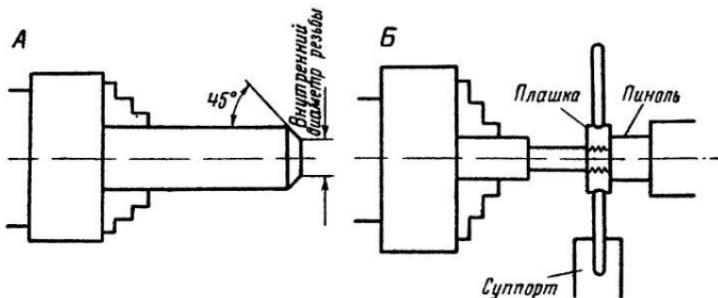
Нарезание резьбы плашкой на токарном станке: А — подготовка заготовки; Б — предупреждение перекоса плашки.
